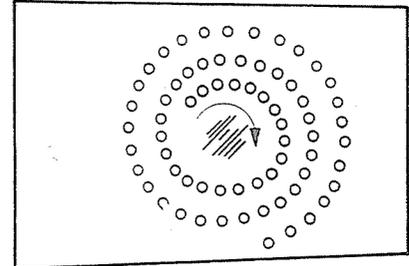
Beim Richten von Blechtafeln sind die Hammerschläge spiralförmig zu führen
